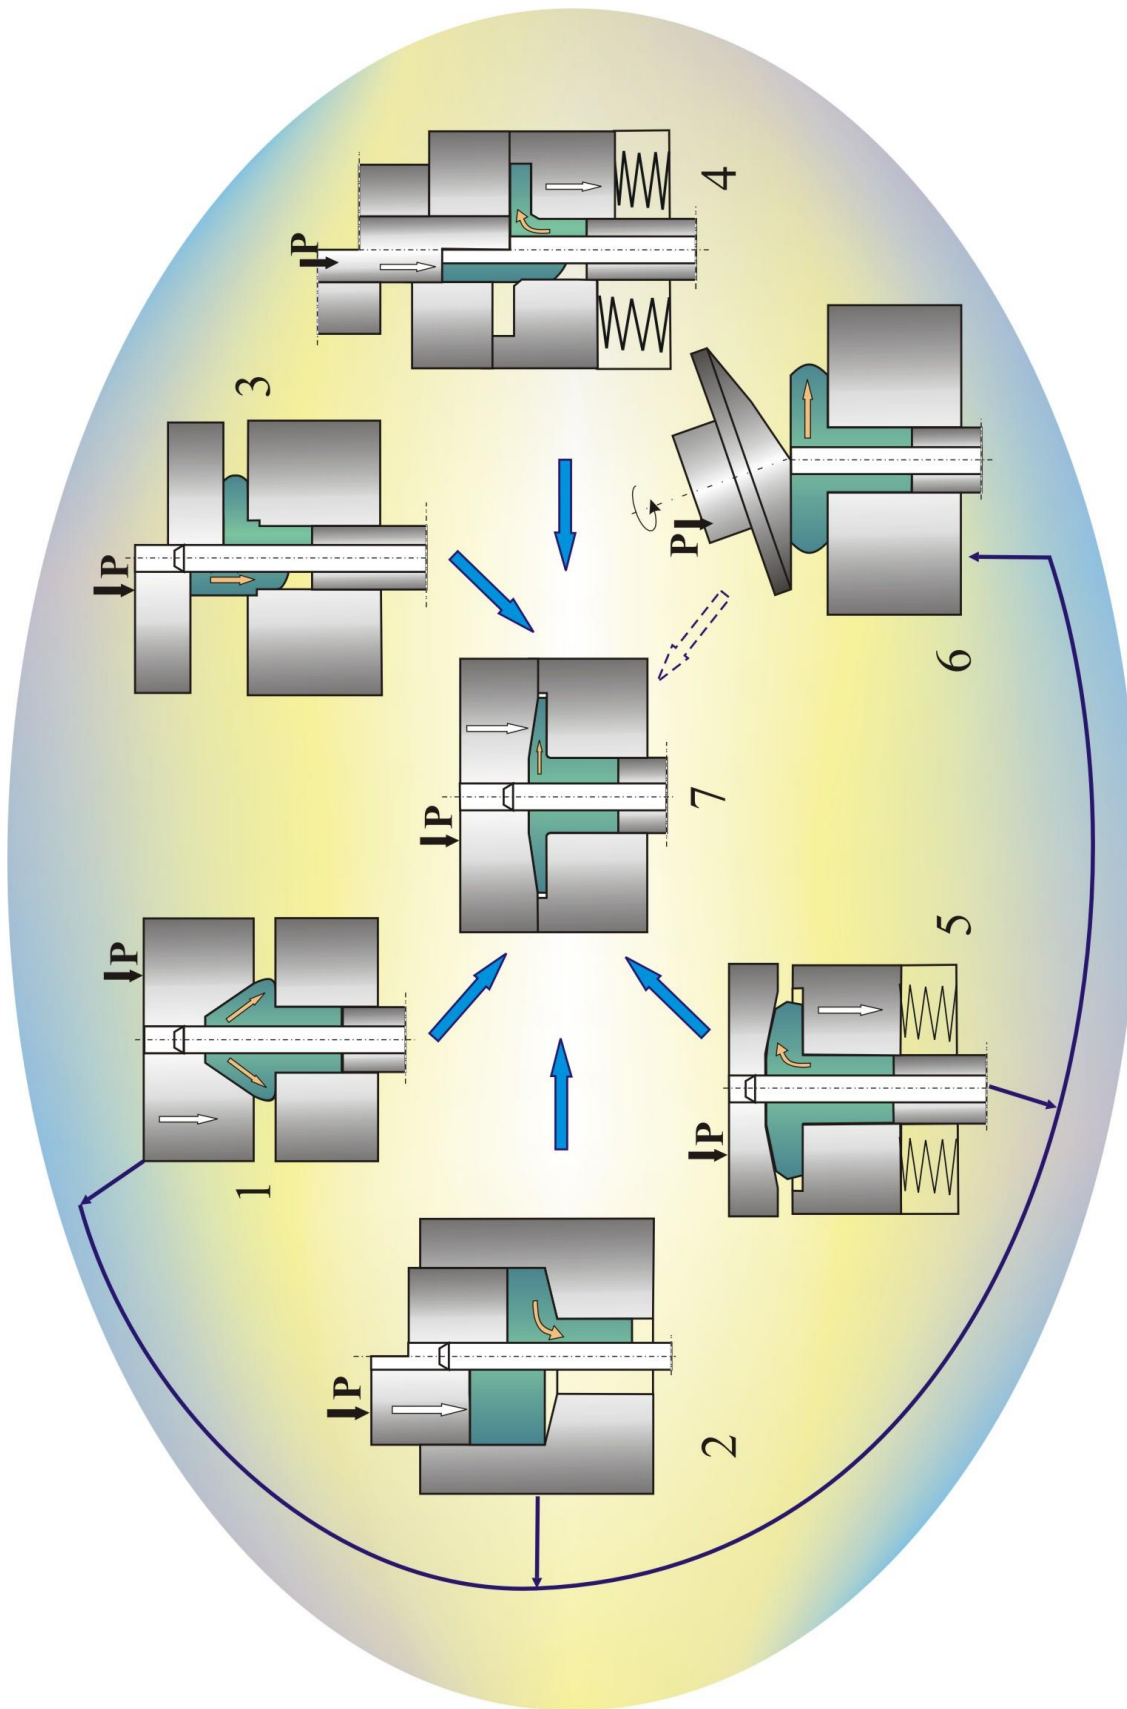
Маршрутная карта (технологические варианты) изготовления детали типа втулки с фланцем из исходной полый заготовки
